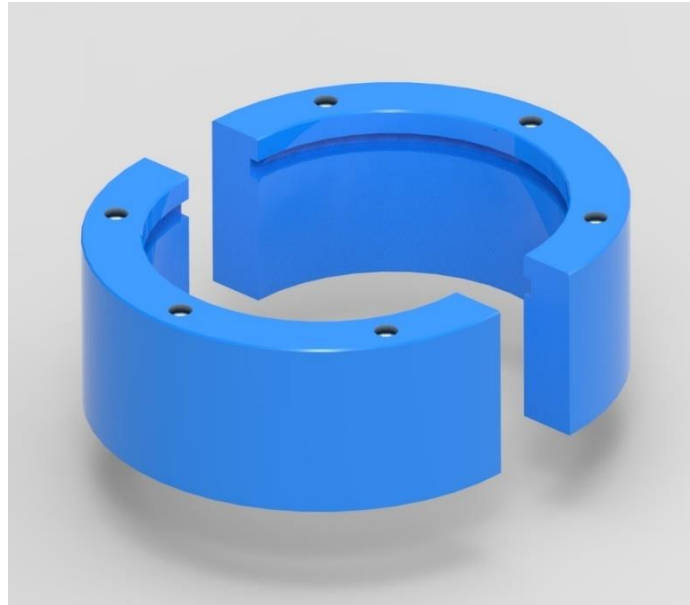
Přípravek pro usazení bočnic [Autor]
